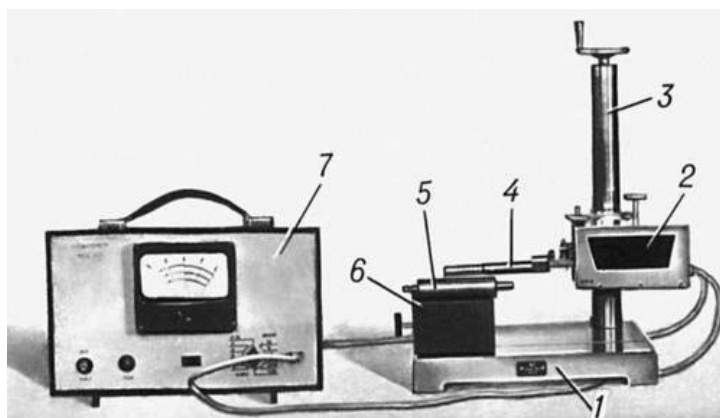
Внешний вид профилометра для контроля шероховатости: 1 – основание прибора; 2 – индикатор; 3 – стойка; 4 – устройство измеряющее; 5 – образец/деталь; 6 – блок установочный; 7 – блок питания
